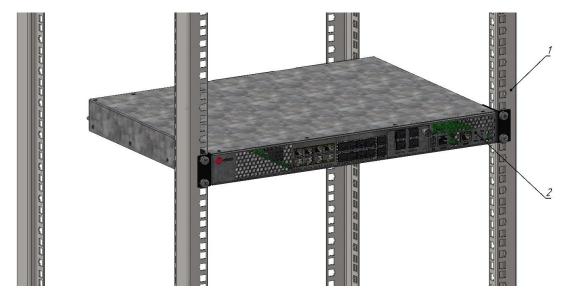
Установка маршрутизатора QSR-3200-8TC6X-AC-AC в стандартный шкаф
